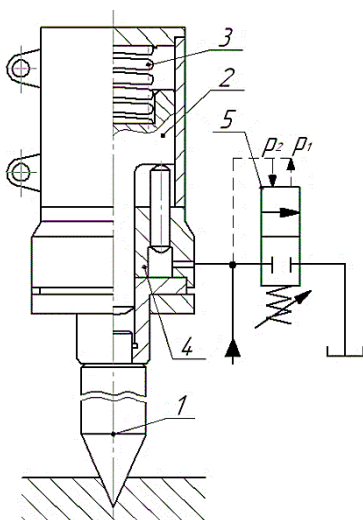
Принципова схема віброударного пристрою на базі гідроімпульсного привода для руйнування гірських порід
